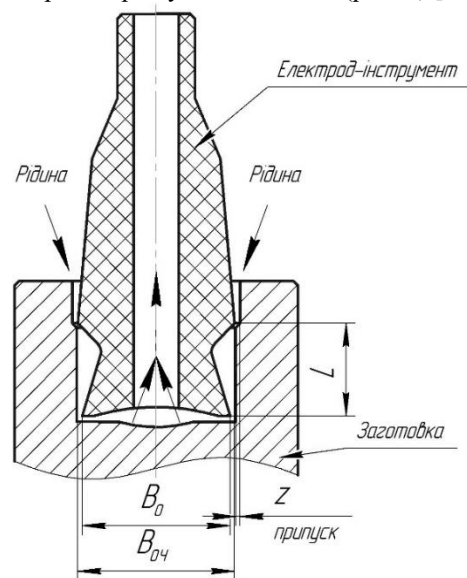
Конструкція ЕІ з двома робочими кромками
